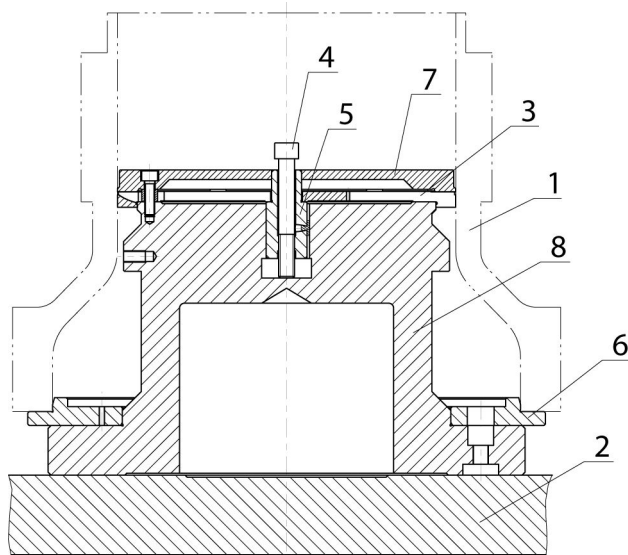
Flachdorn-Spannzeug auf Maschinentisch für Getriebeglocke
